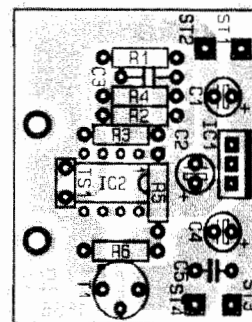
Bestückungsplan der Steuerung. TS 1 wird über Zuleitungen angeschlossen oder seitlich abgewinkelt.
